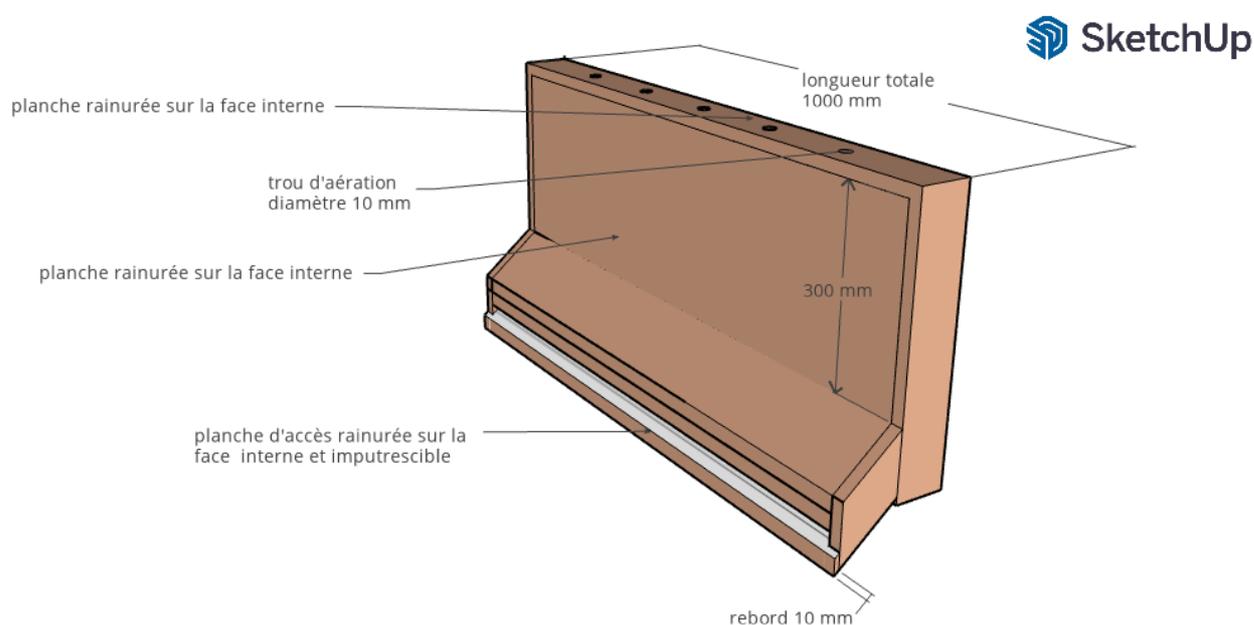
Plan des gîtes installés dans les bâtiments, vue générale.
